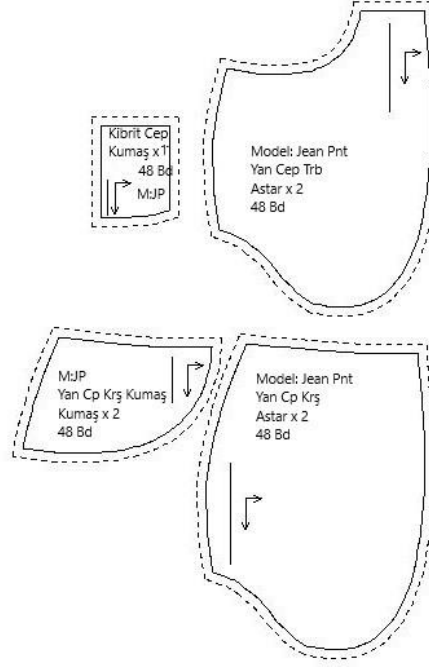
Jean Pantolonda Yan Cep Oluşturulması
